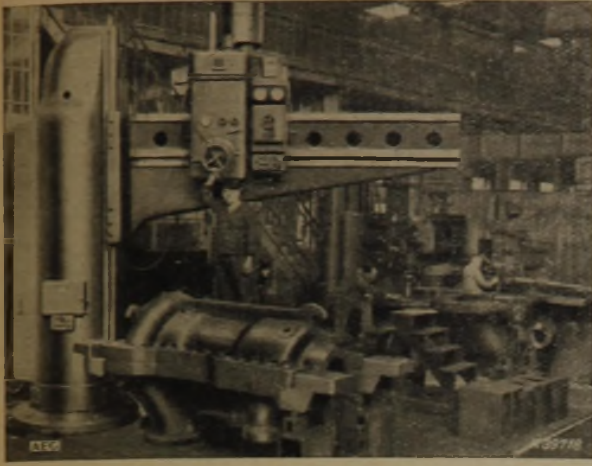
Gehäuseteile während des Bohrens der Teilflugschraubenlöcher mit Radialbohrmaschinen (Werkfoto AEG)
